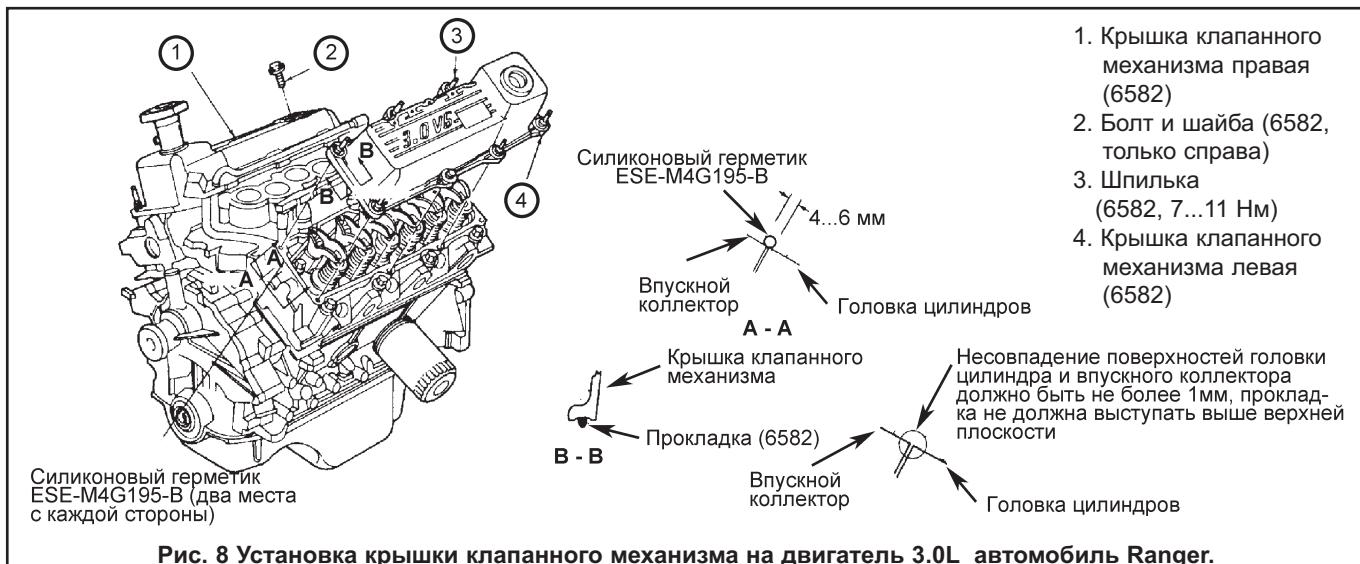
Установка крышки клапанного механизма на двигатель 3.0L автомобиль Ranger.
